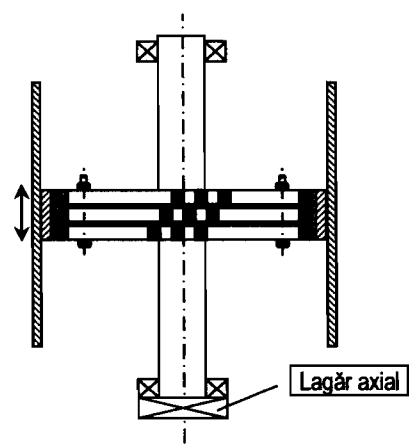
Motor magnetic cu ax vertical, cu un grup rotoric
